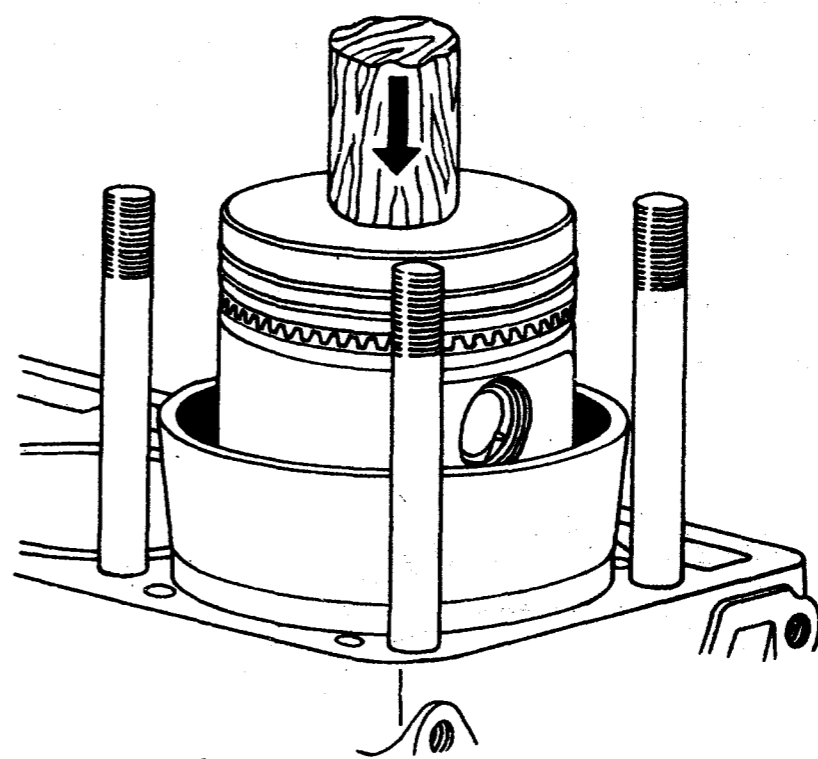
Постановка поршней с кольцами в цилиндр с помощью приспособления 5-Y-III06
